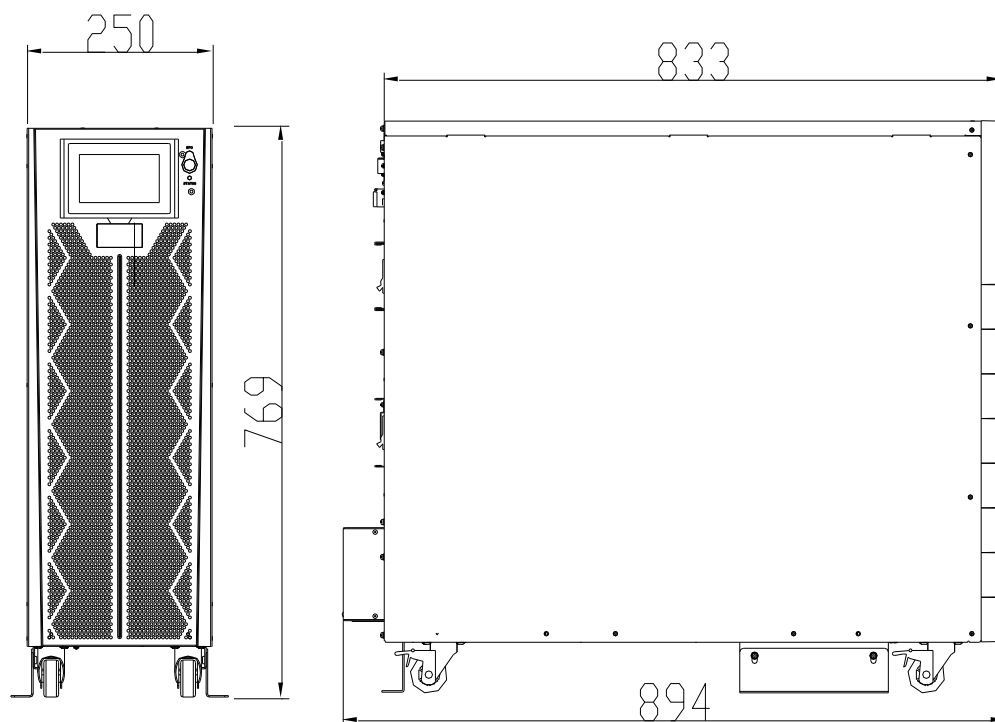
Размеры ИБП 40kVA (стандартный типоразмер)
